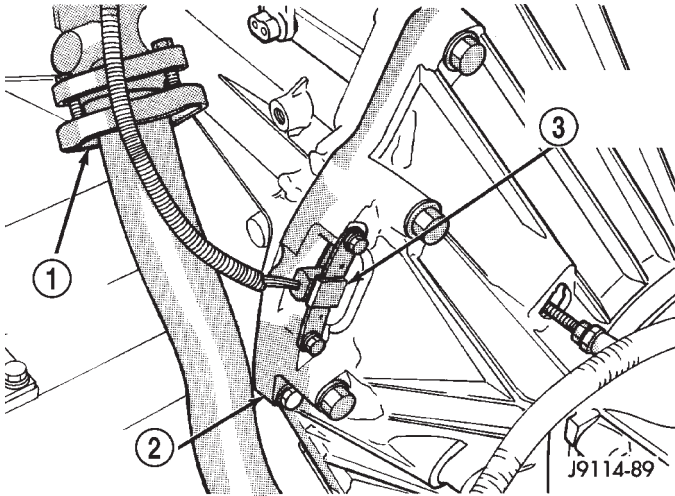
Sensor de posición del cigüeñal - Motor 2.5L
